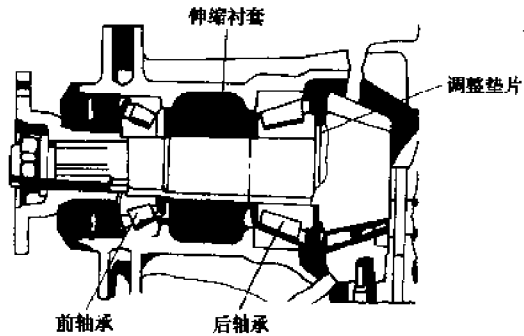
主动圆锥齿轮轴承预紧度的调整方法之二
